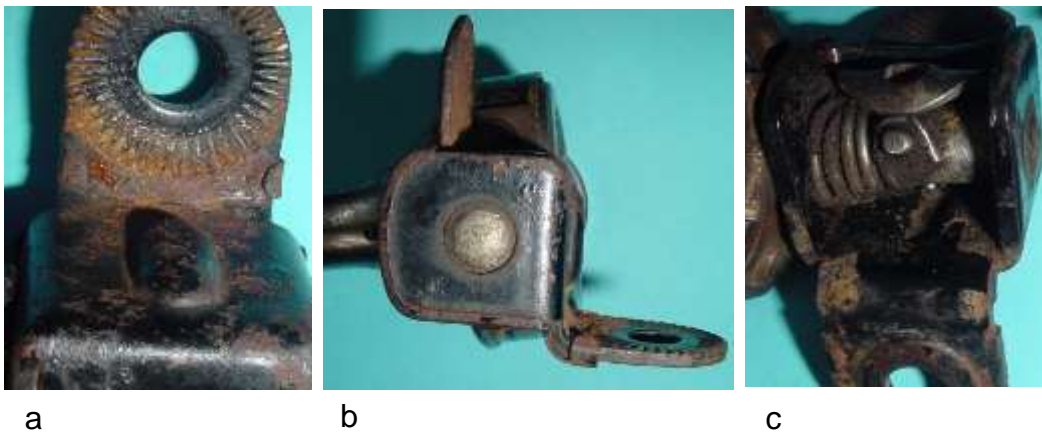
Kippvorrichtung: a) Basisblech mit Bohrung für die Halterbefestigung, b) Bedienungshebel, Drehbolzen und Halterbefestigung, c) Drehbolzen mit Druckfeder
